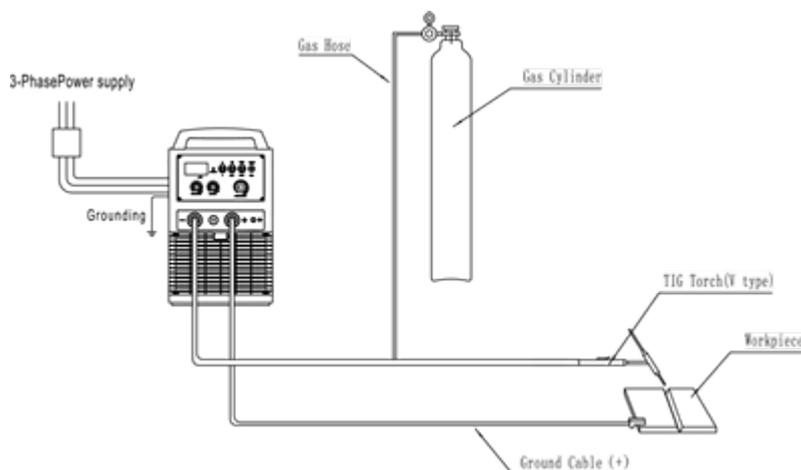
TIG сварка (простая TIG)
